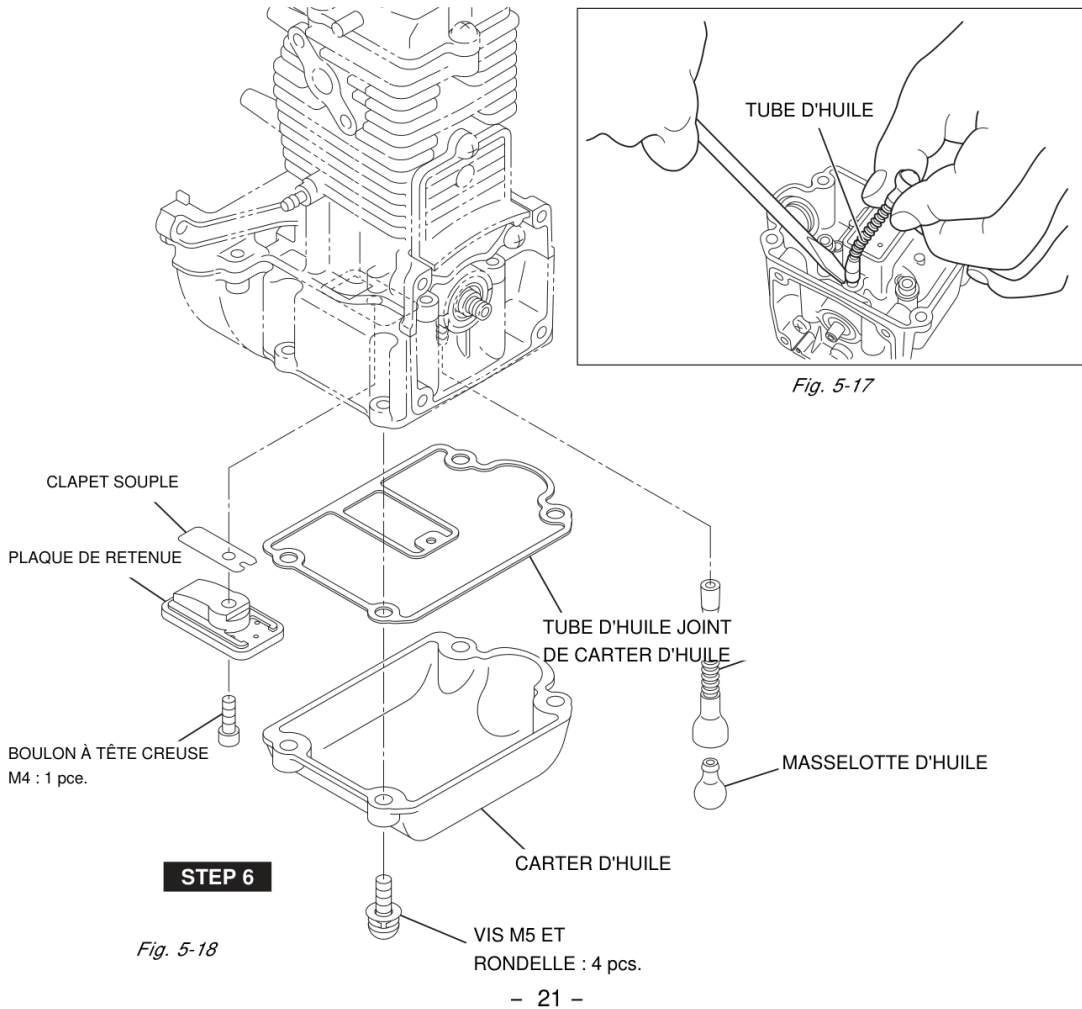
/ 5-18 — Étape 6 : carter d'huile et tube d'huile
